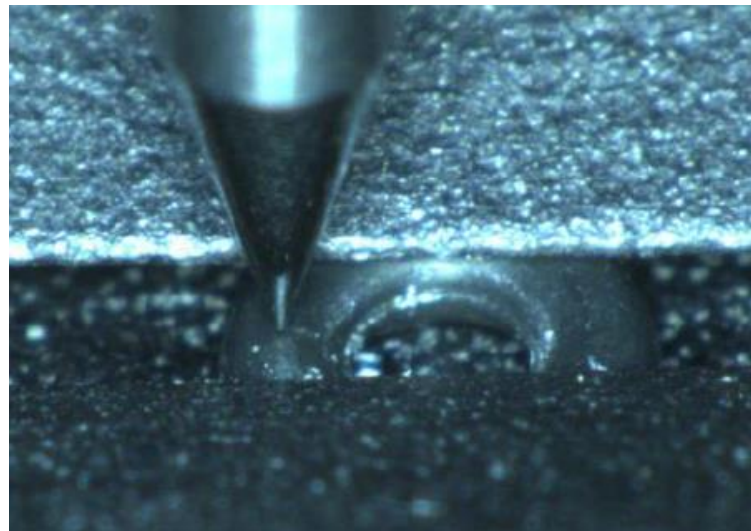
Härtemessung eines O-Ringes mit einem Durchmesser von 0,5 mm mit Hilfe des LNP® nano touch (Bild: O-Ring Prüflabor Richter)
